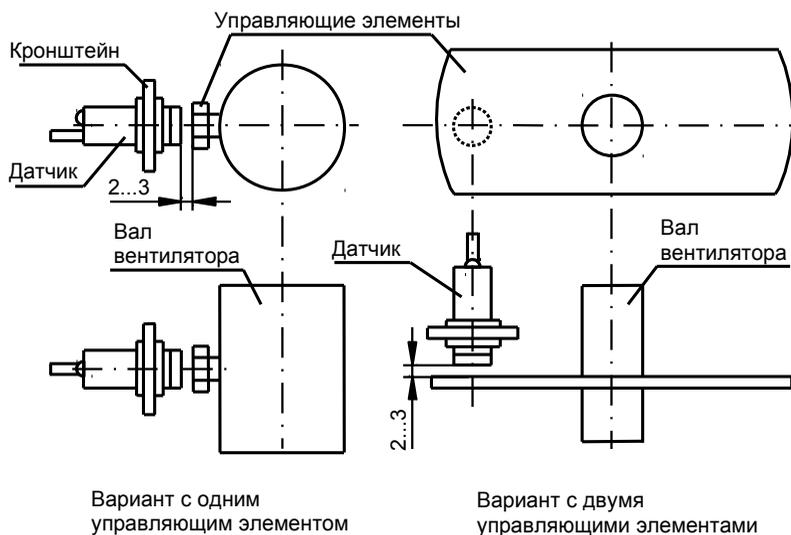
Регулировка рабочего зазора датчика вентилятора
